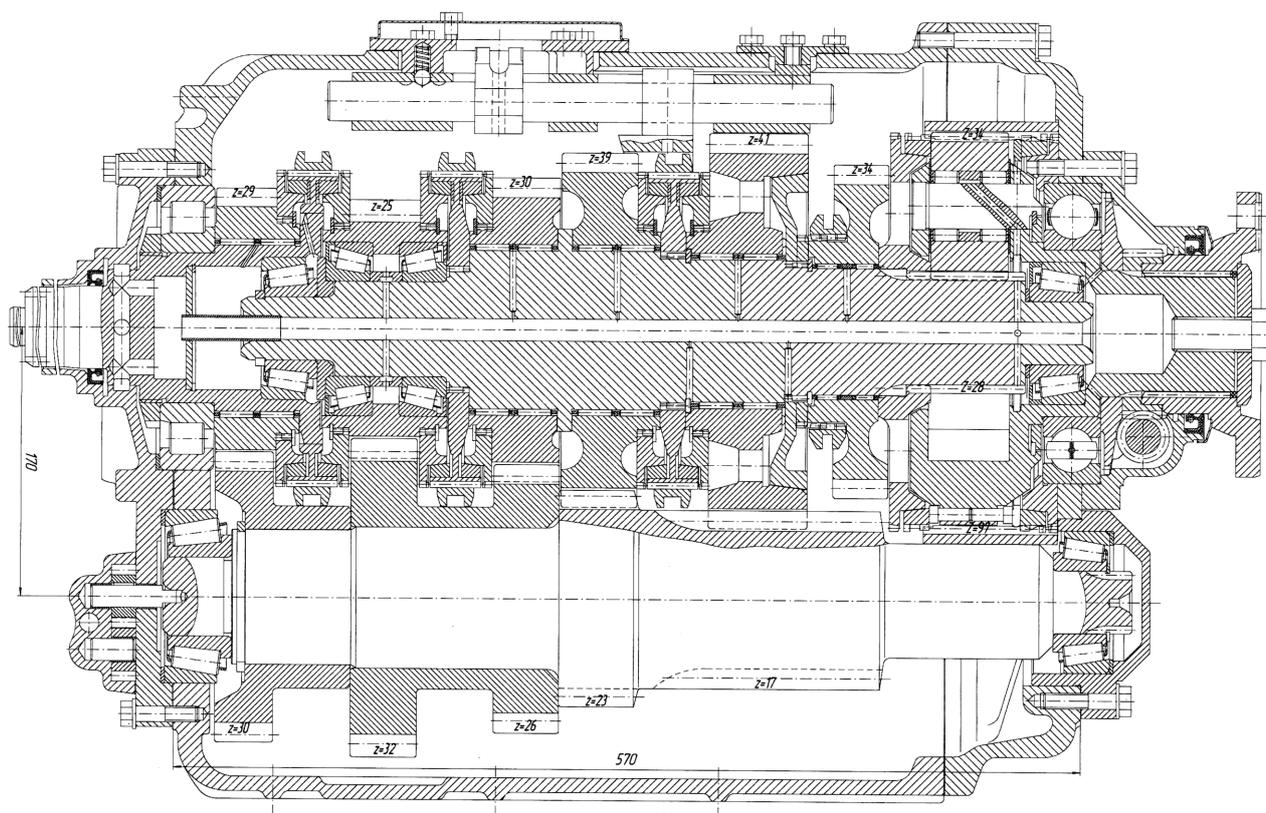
Коробка передач ТМ16-2000 (продольный разрез)
